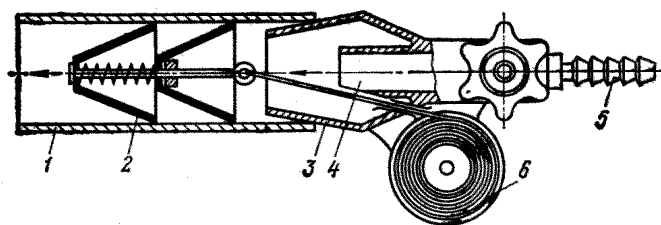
Пневматическое приспособление для затяжки шнура в блок 1 — труба; 2 — поршень; 3 и 4 — сопла; 5 — штуцер для воздушного шланга; 6 — катушка с тросиком или капроновым шнуром
